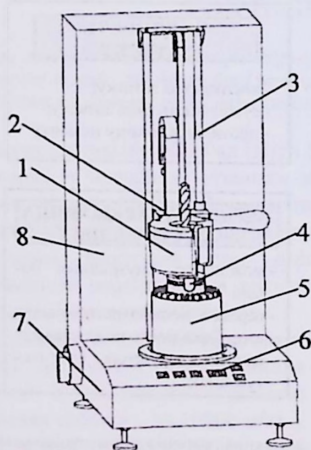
Спеціальний пристрій для термозатиску інструмента ISG2000 фірми Bilz: 1 – котушка індукційного нагрівання; 2 – каретка; 3 – напрямні; 4 – затискний патрон; 5 – пристрій для закріплення затискного патрона; 6 – пульт керування; 7 – основа; 8 – стійка.
